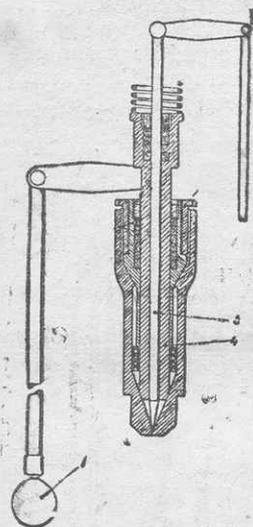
Форсунка компрессорного автомобильного двигателя «Майбах».
